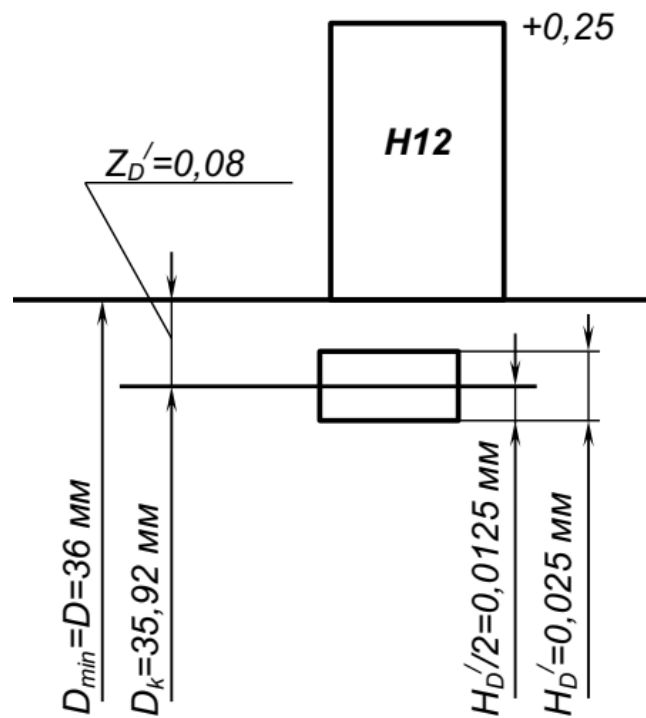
Схема расположения полей допусков комплексного калибровки по наружному диаметру шлиц
